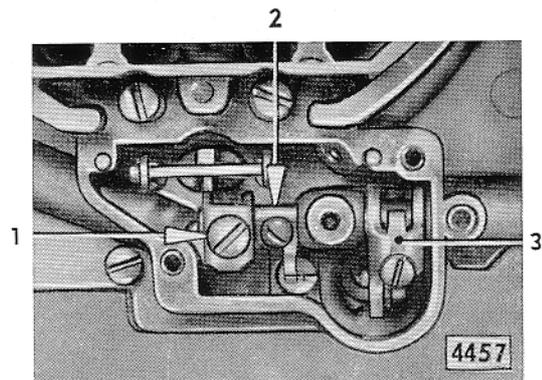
Feststellschrauben für Belüftungs-, Pumpen- und Teillastnadelbetätigungshebel
